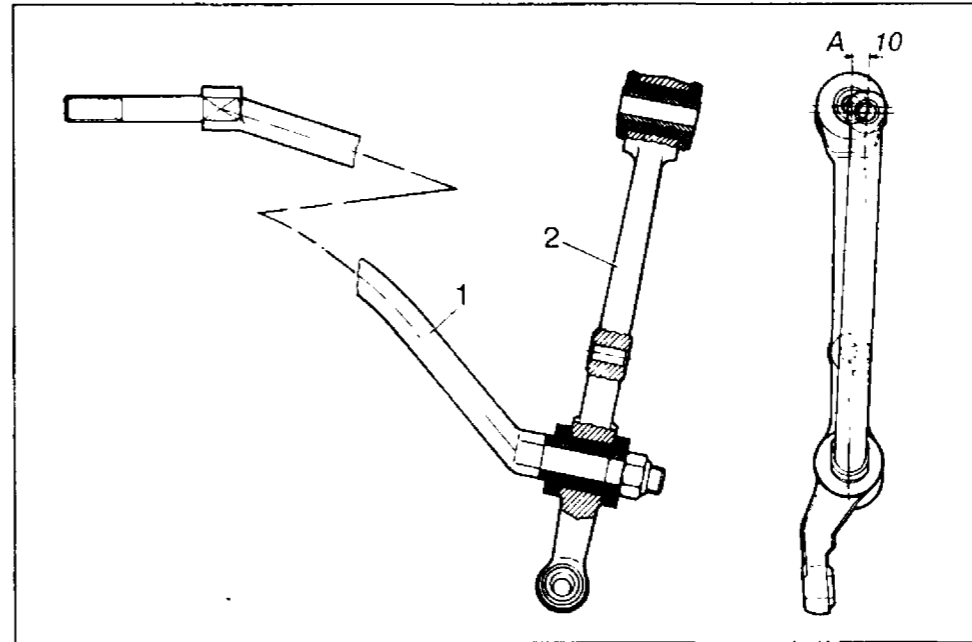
Сборка рычага подвески с растяжкой: 1 — растяжка; 2 — рычаг подвески
